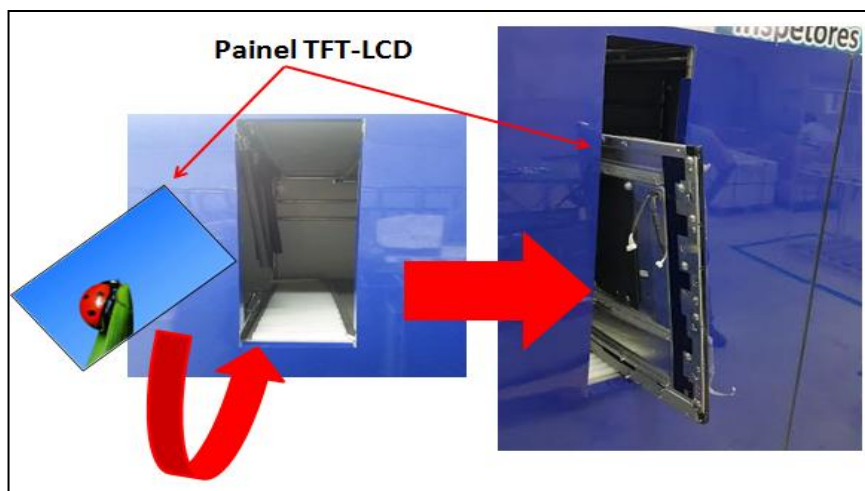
Inspeção do painel TFT-LCD na plataforma para inspeção automática.
